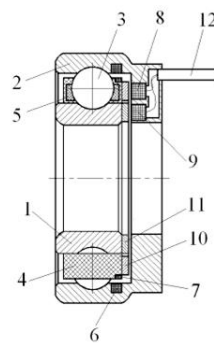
Конструкция подшипника с управляемой кинематикой
